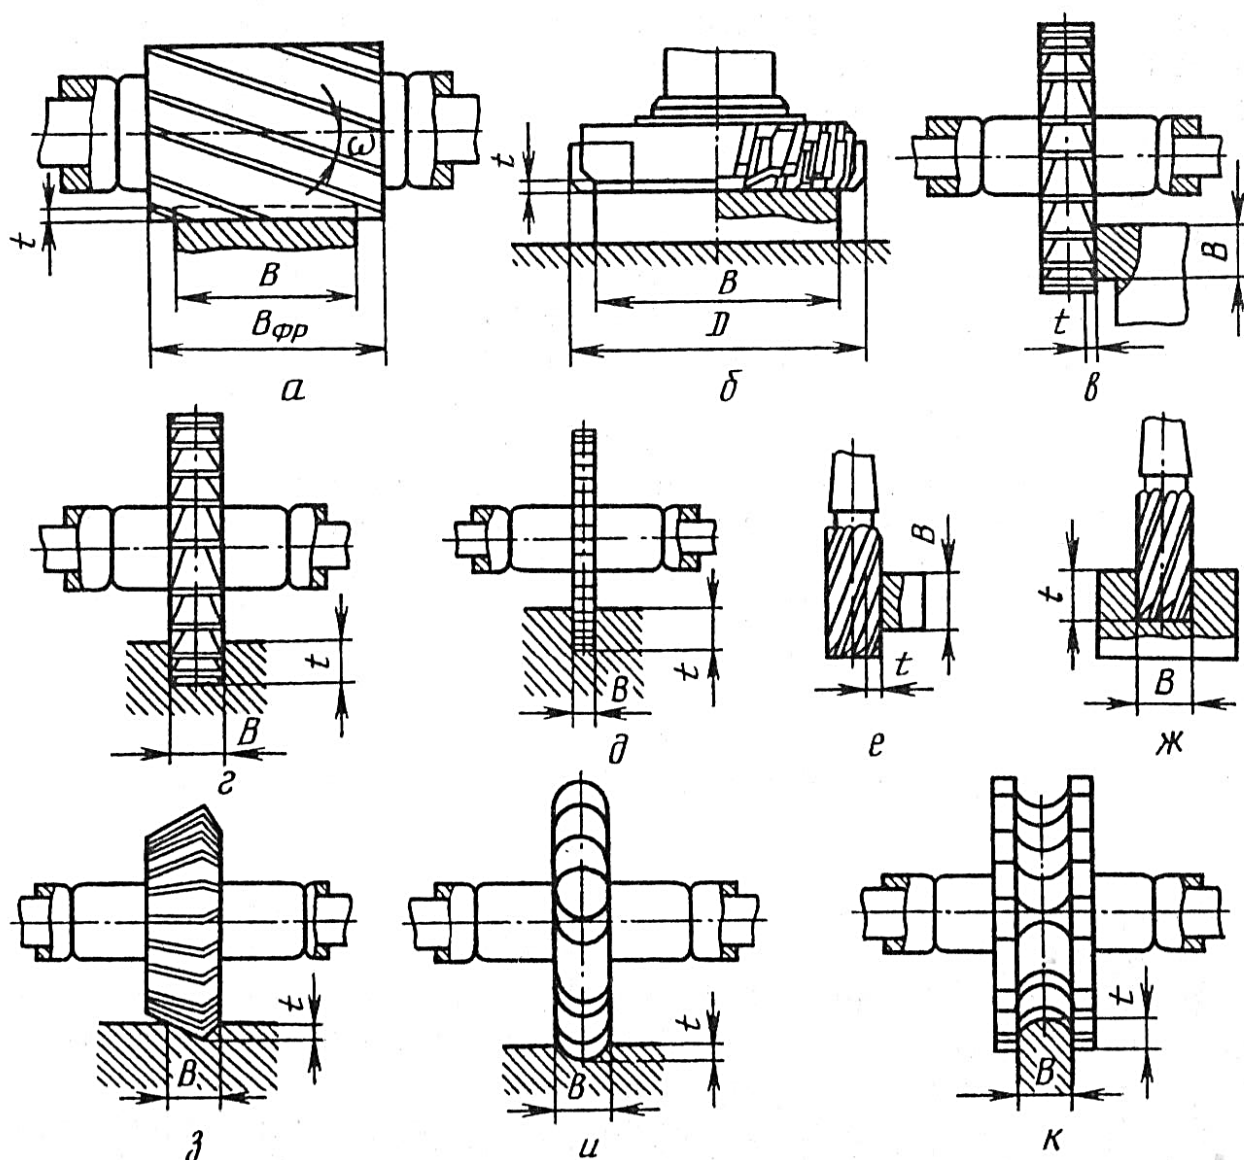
Типы фрез и элементы режима резания: а - цилиндрические; б – торцевые; в, г – дисковые трёхсторонние; д – прорезные и отрезные; е, ж – концевые; з – угловые; и, к – фасонные с выпуклым и вогнутым профилем;  $B$  – ширина фрезерования;  $t$  – глубина резания;  $D$  и  $B_{фр}$  – диаметр и ширина фрезы;  $\omega$  – угол наклона винтовой канавки
